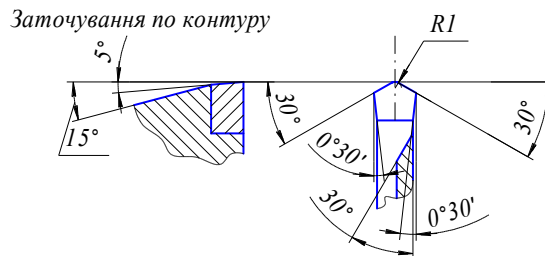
Форма заточування кільцевого свердла з прямокутними гвинтовими канавками
